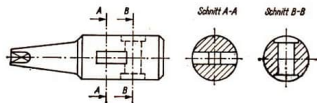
Bohrmesseraufnahme mit Spiralkeileinspannung
